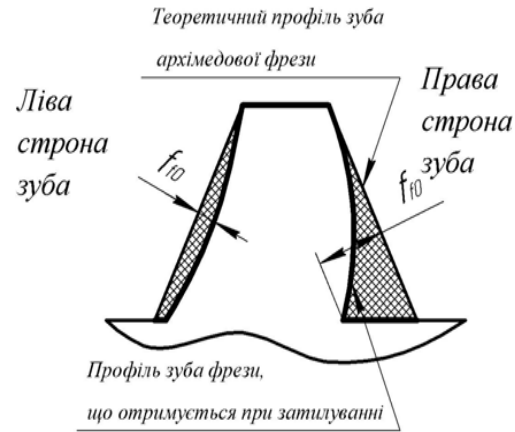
Похибки профілю зуба фрези при затилуванні конічною поверхнею круга
